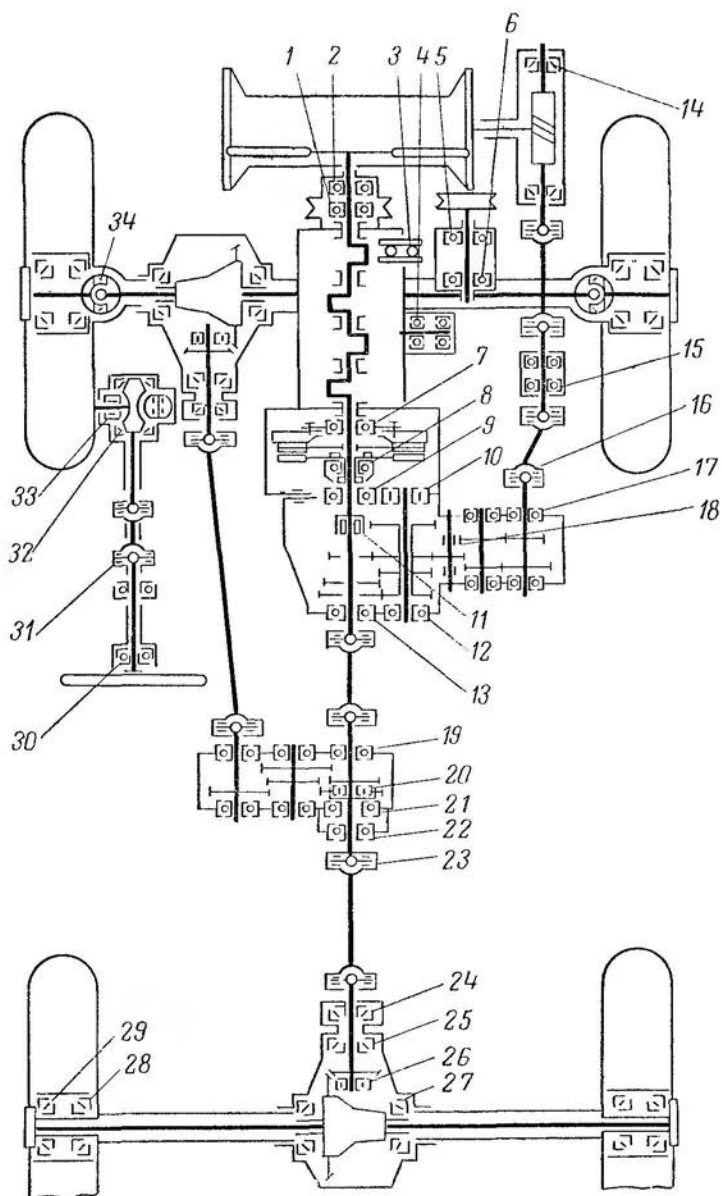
Схема расположения подшипников автомобиля ГАЗ-66-02
